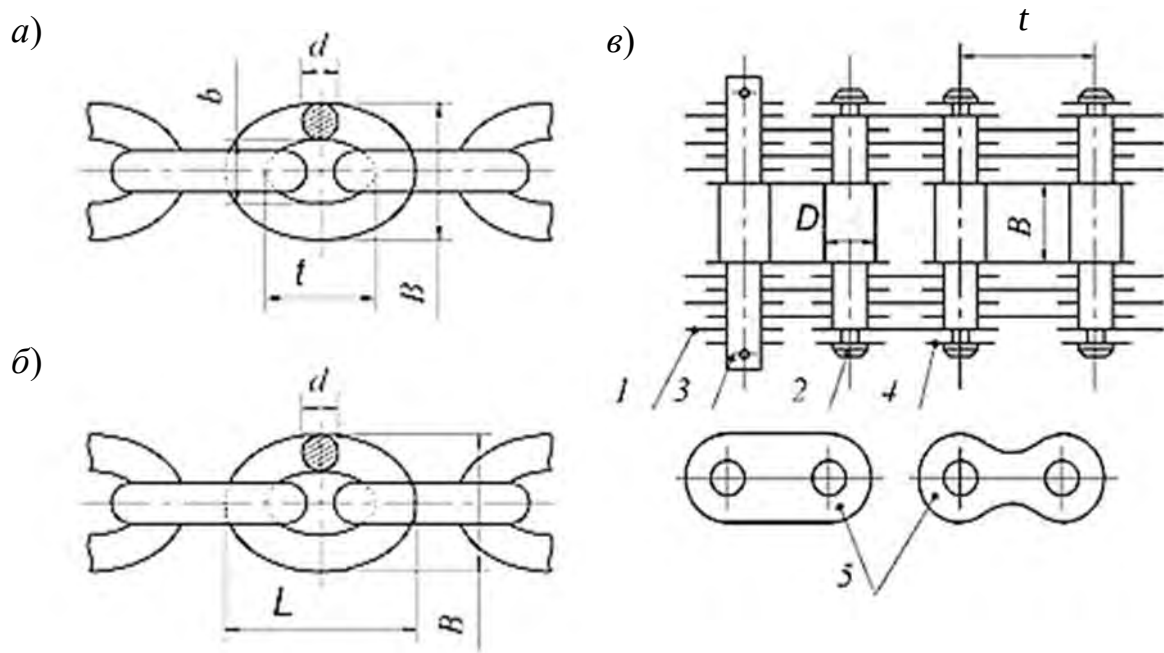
Грузовые цепи: a – сварная калиброванная; b – сварная некалиброванная; $в$ – пластинчатая шарнирная; 1 – пластина; 2 – валик; 3 – валик разъема; 4 – шайба; 5 – типы пластин: простая и фасонная
